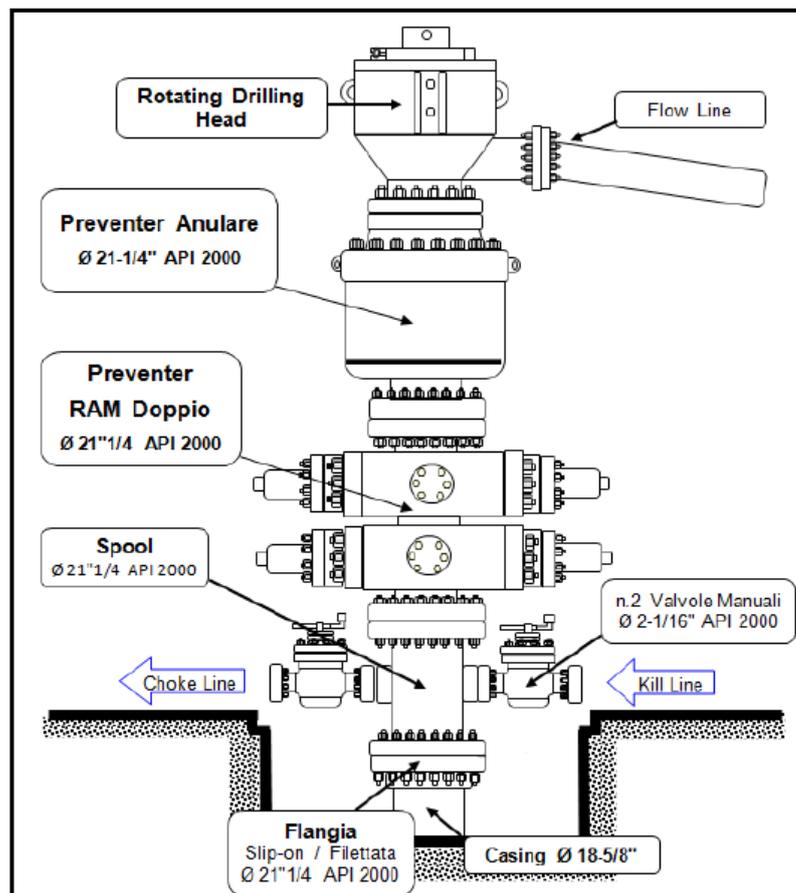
a Esempio di Testa Pozzo in Fase di Perforazione
